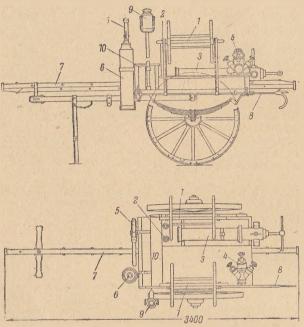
Реквизитный ручной двухколесный рессорный ход.
